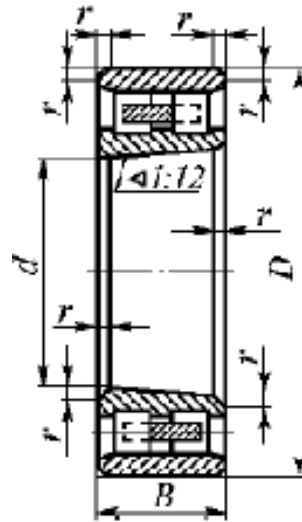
Роликовий радіальний двохрядний підшипник з короткими циліндричними роликами, серії 3182100
